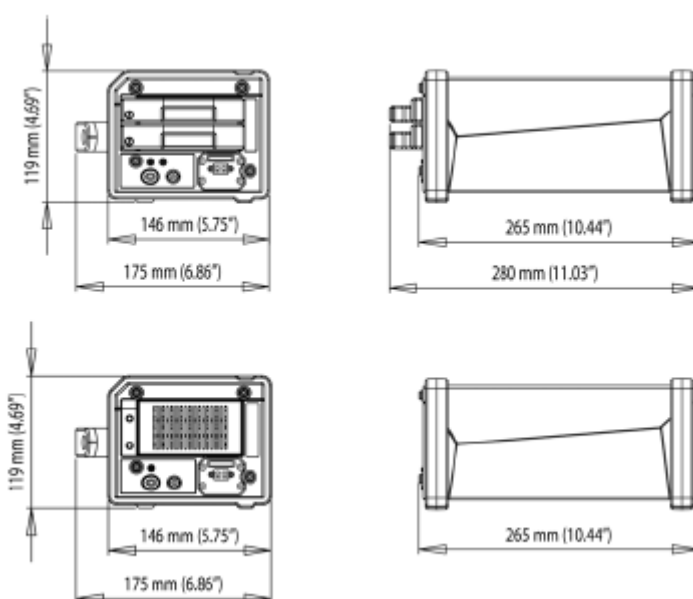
Модули передатчика ISOBE5600t (сверху) и ISOBE5600tm (снизу), размеры
